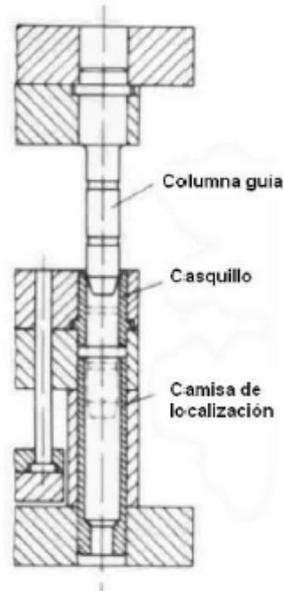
Plano detalle columna guía, casquillo y camisa de localización.
